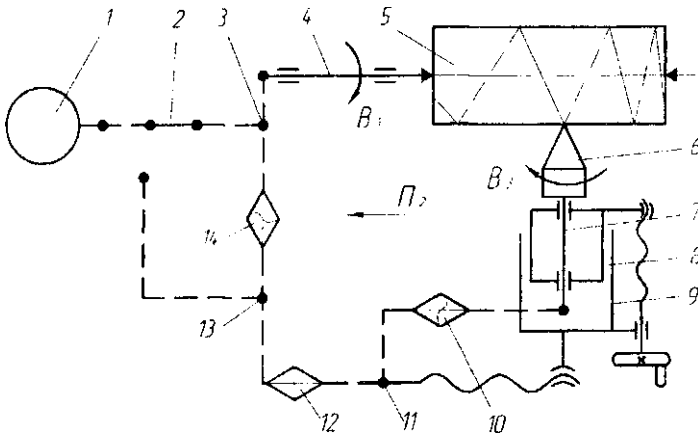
Структурная схема станка для обработки винтовых поверхностей переменного шага
